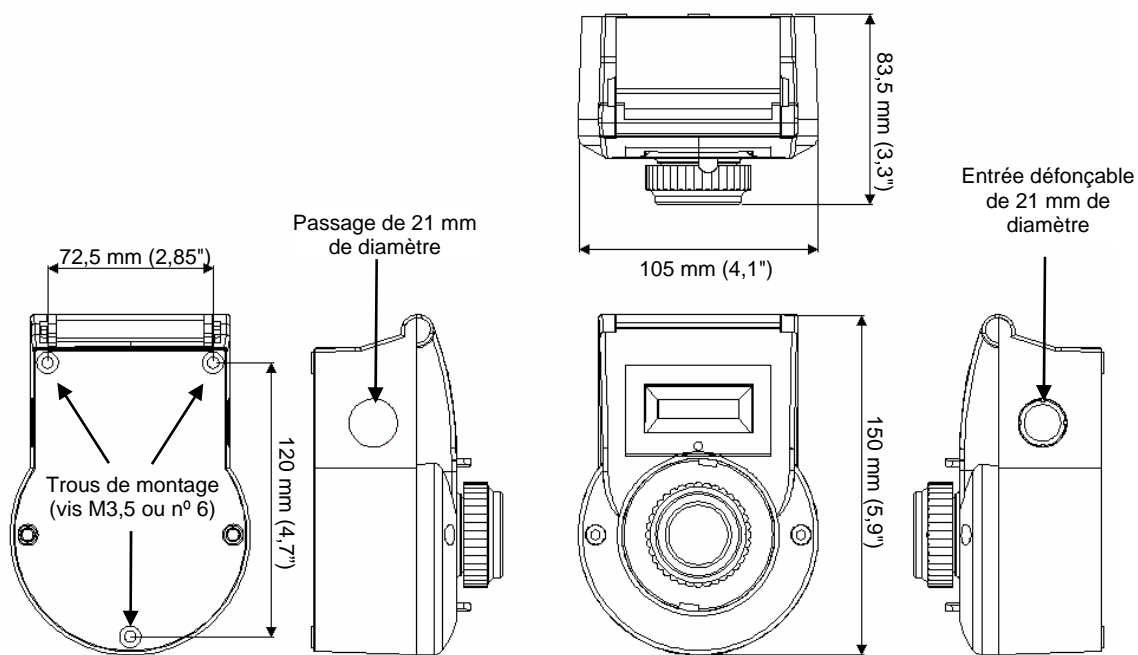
Dimensions du détecteur et emplacement des trous de montage
